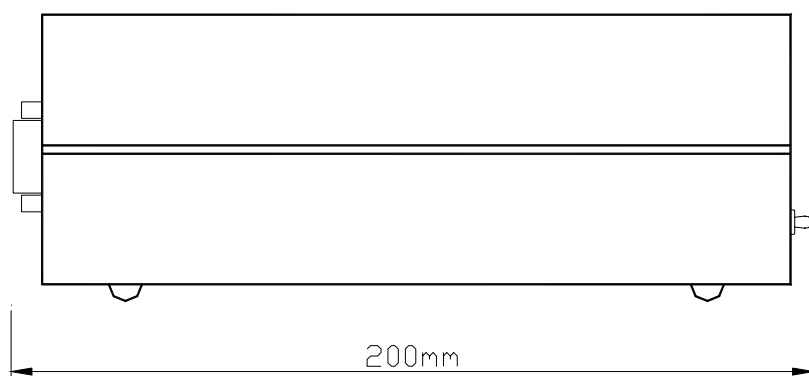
Внешний вид и габаритные размеры изделия ДСВ-4
